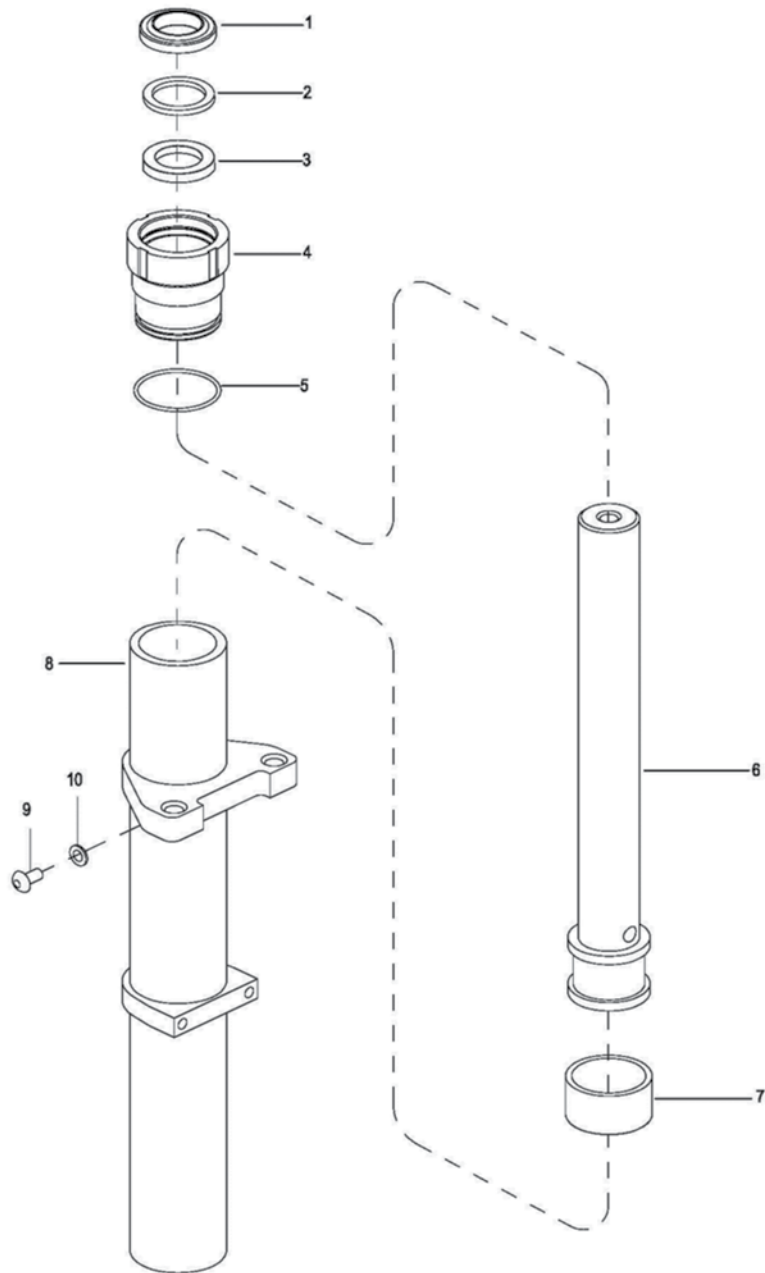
CYLINDRE DE MONTÉ (TÉLESCOPIQUE)
